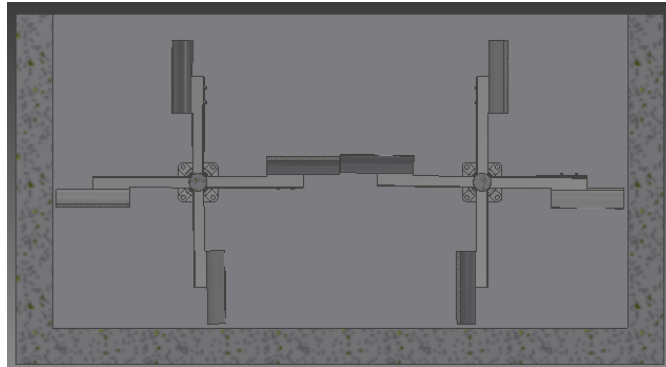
Soldadura de las paletas al eje del mecanismo
